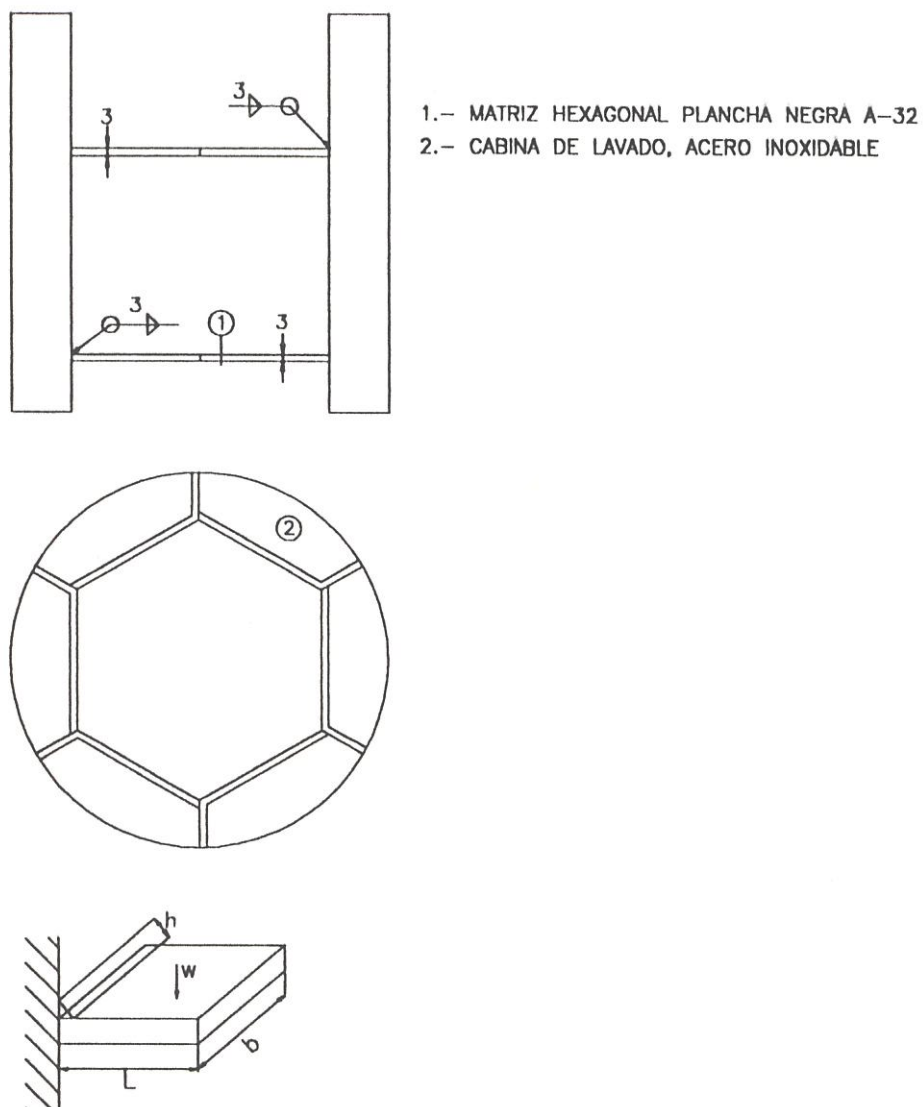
Esquema de Soldadura de la Matriz Hexagonal con la Cabina de Lavado
